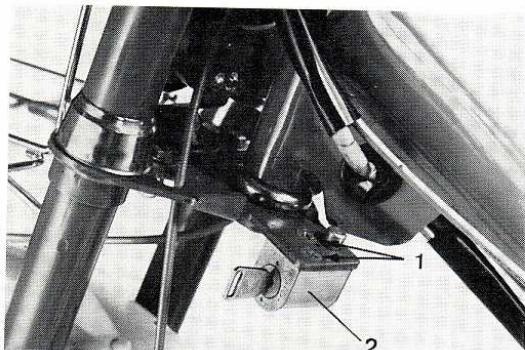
DEMONTAGE DE LA SERRURE DE DIRECTION.
